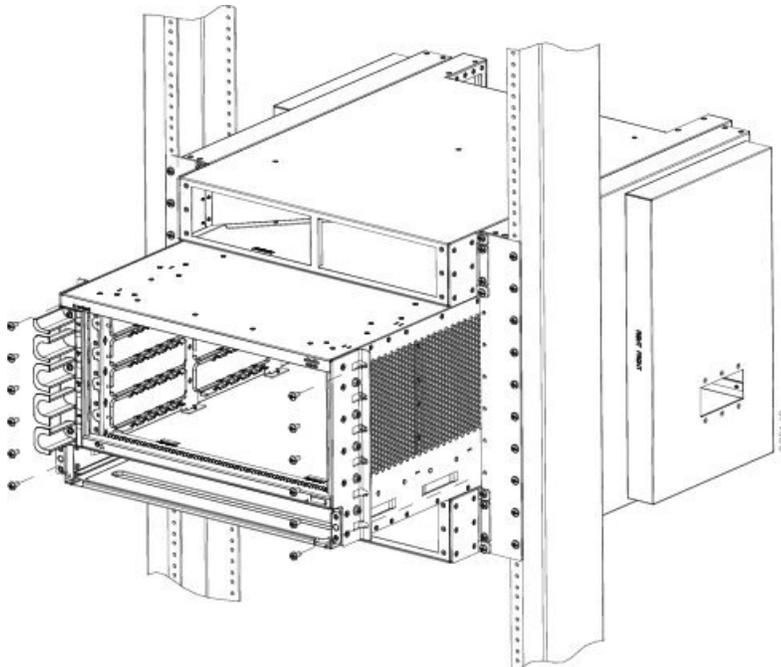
Befestigung der Seitenleitbleche des Cisco ASR 9904-Router-Chassis an den Luftumlenkern (Rückansicht)
